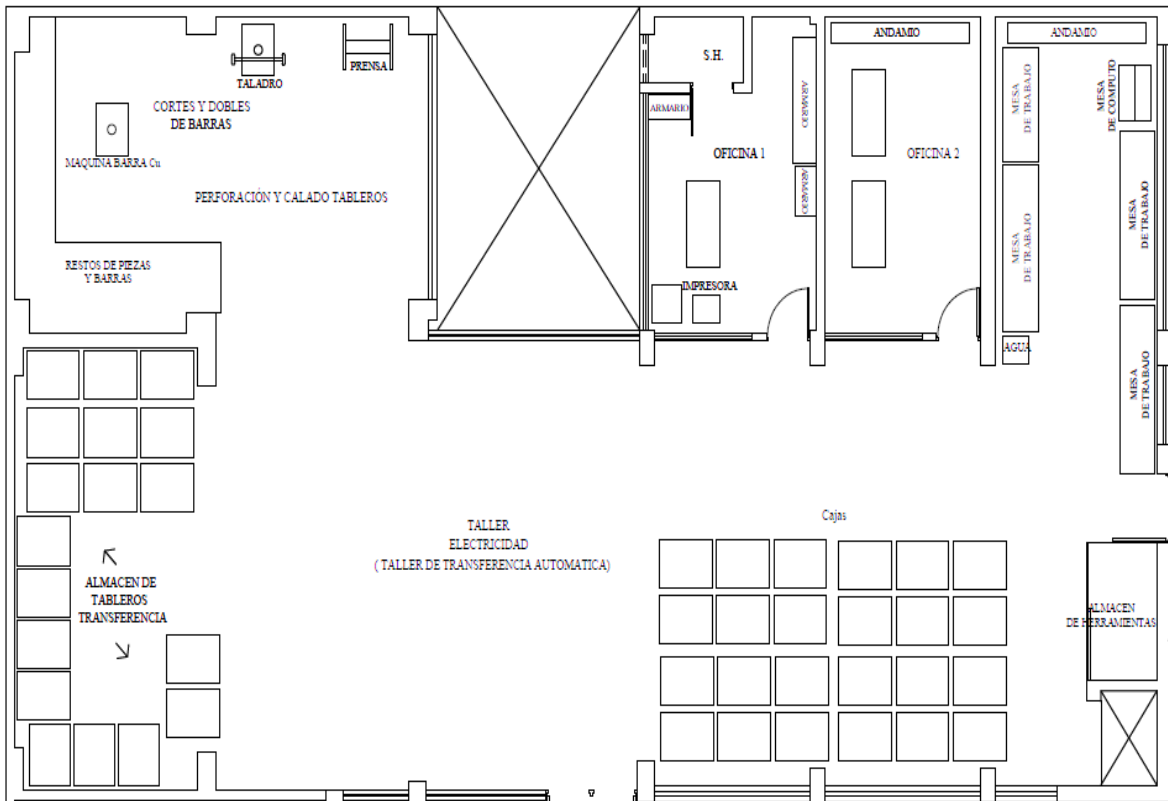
Distribución de planta fabricación de tableros de transferencia automática (antes).
